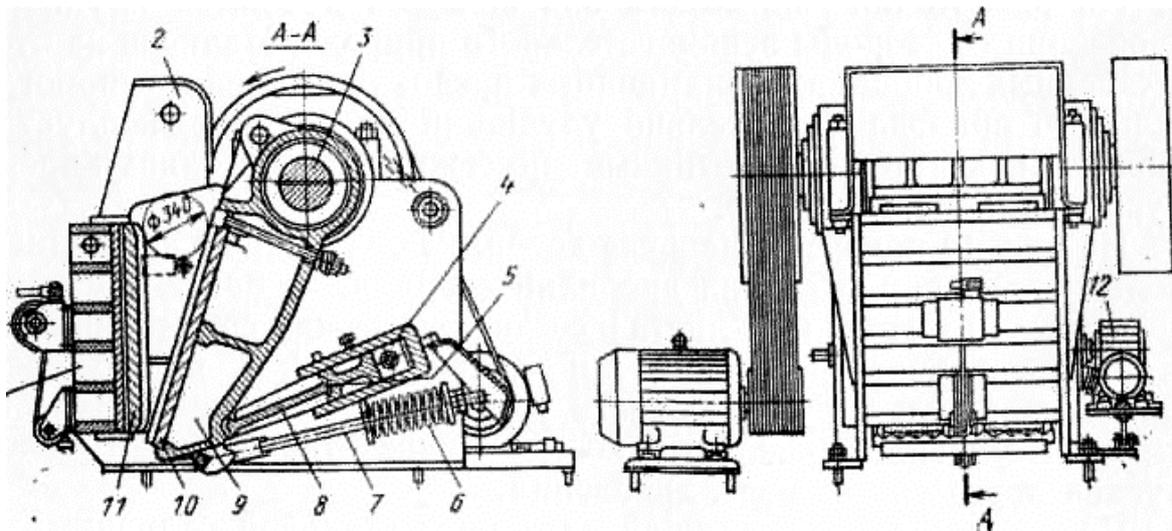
Конструкция щековой дробилки со сложным движением щеки
